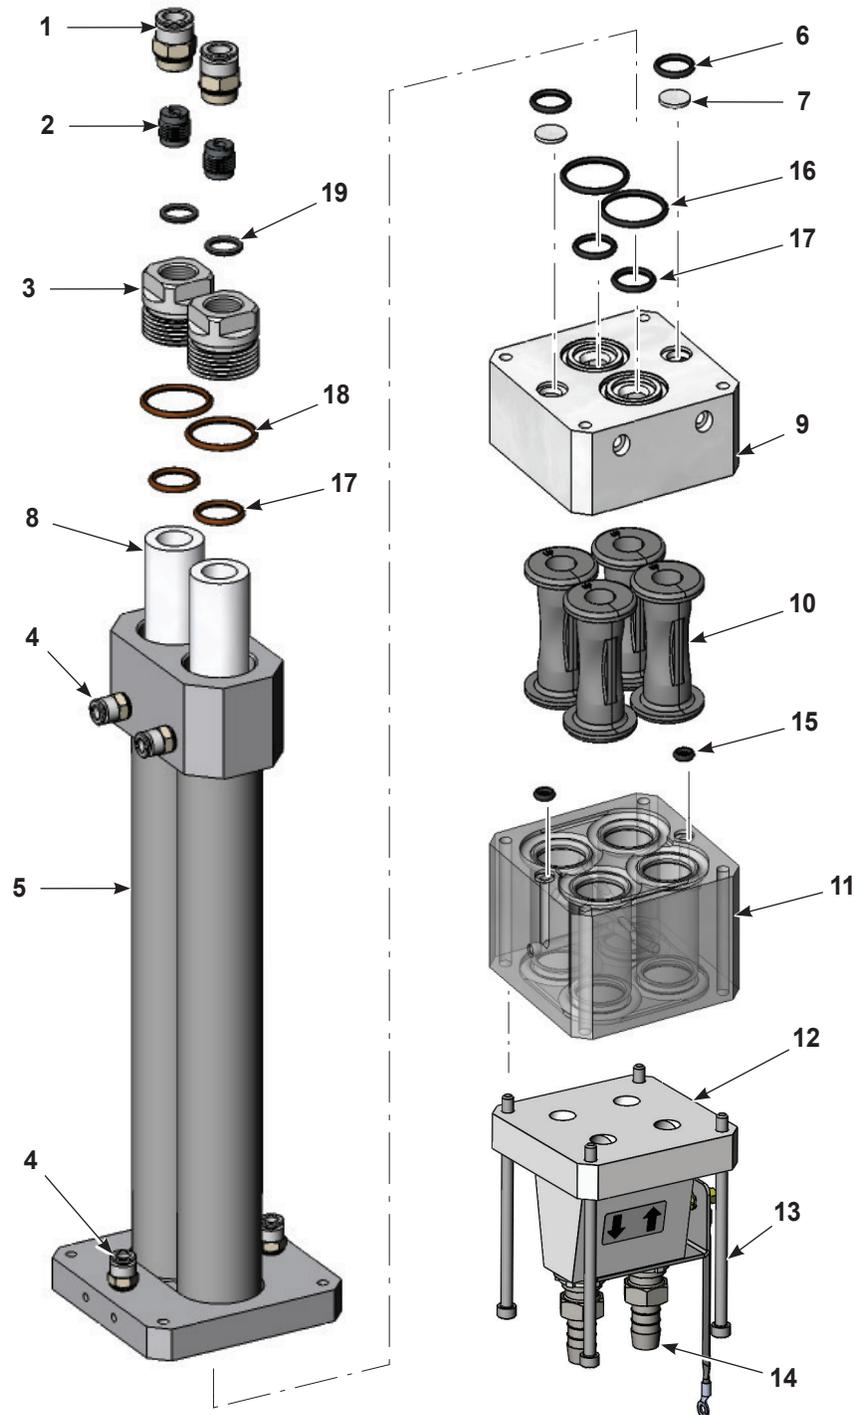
Baugruppe Pumpe ohne Steuerelemente
